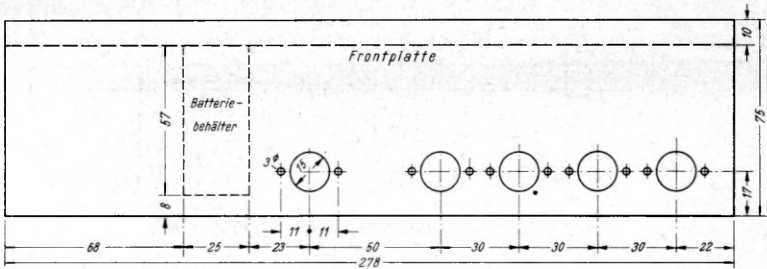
Maßskizze mit Ausschnitten für die Chassistrückseite
